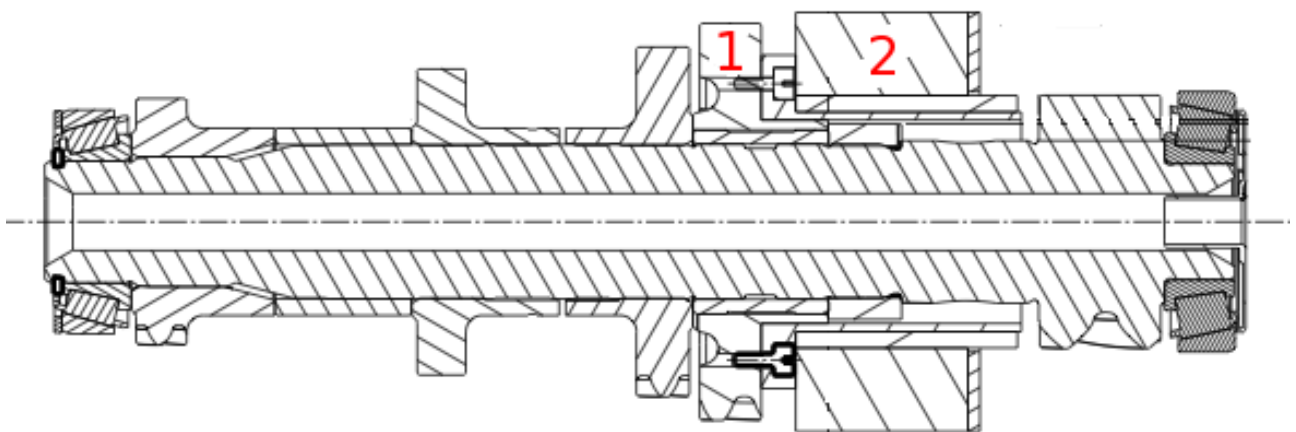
Plan de l'arbre secondaire avec le pignon fou instrumenté.
